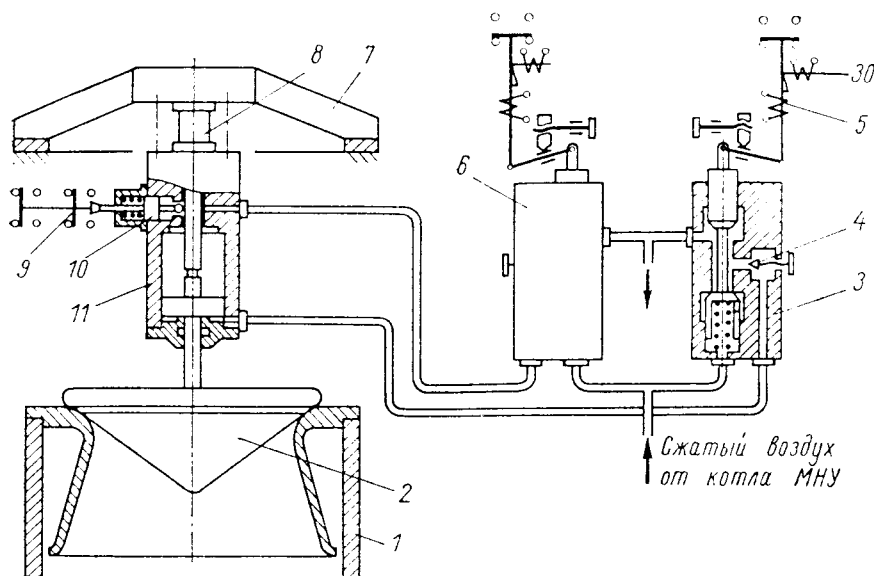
Схема устройства впуска воздуха в камеру рабочего колеса гидротурбины: 1 — надставка вала генератора; 2 — клапан впуска воздуха; 3 — золотник открытия клапана; 4 — дроссель; 5 — электромагнит с защелкой; 6 — золотник закрытия клапана; 7 — крестовина; 8 — шаровой шарнир; 9 — контакты стопора; 10 — стопор верхнего положения клапана; 11 — сервомотор
